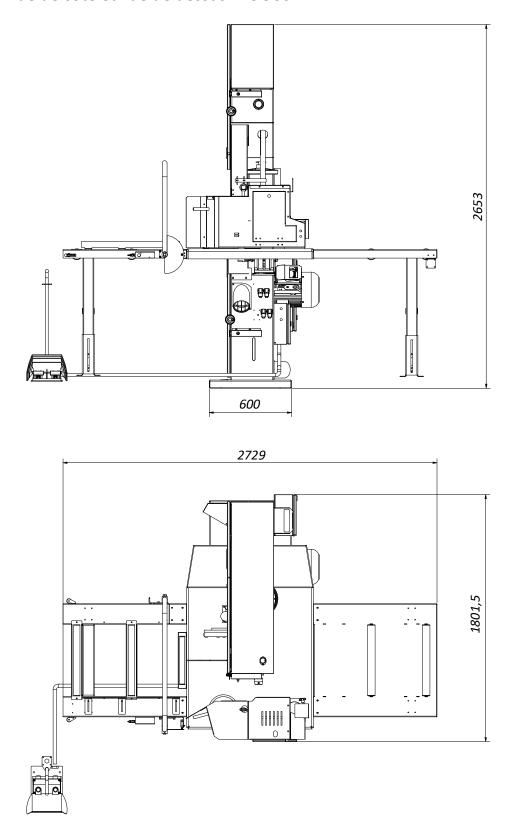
dimensions - vue de côté et vue de dessus TBS 900 R
